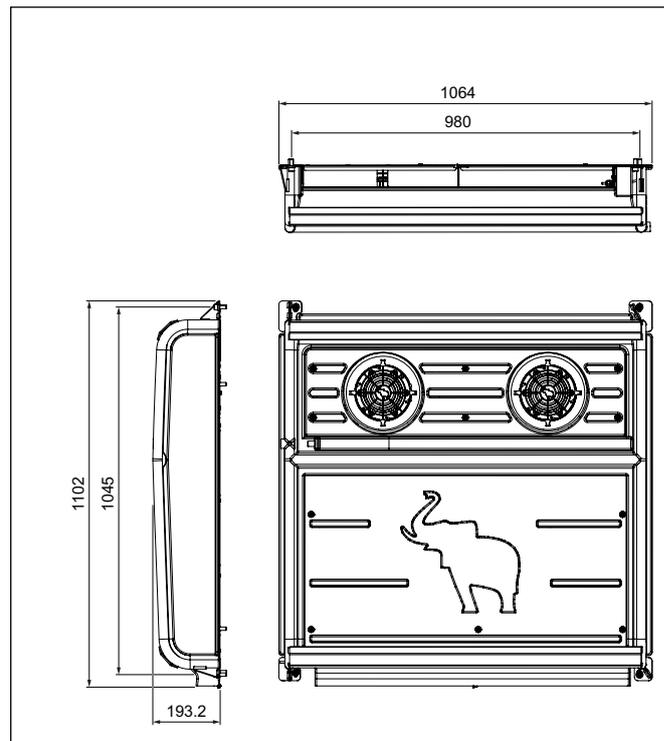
Габаритные размеры потолочного дополнительного испарителя
